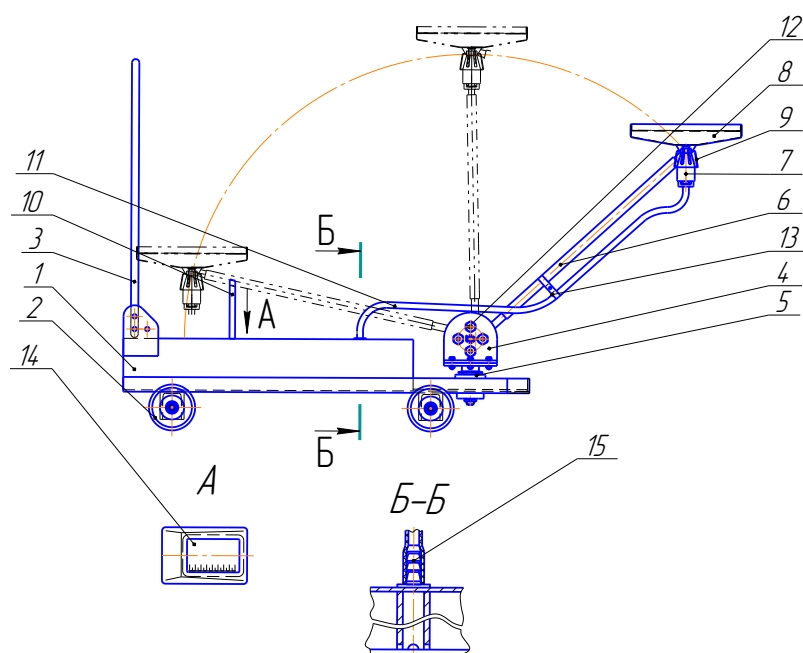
Тележка для слива масла: 1 – рама; 2 – колёса; 3 – складная рукоятка; 4 – храповой узел; 5 – механизм поворота; 6 - штанга; 7 – коннектор; 8 – ванночка; 9 – рычаг; 10 – держатель; 11 – шланг; 12 – регулировочный болт; 13 – хомут; 14 – смотровое окно; 15 – штуцер.
